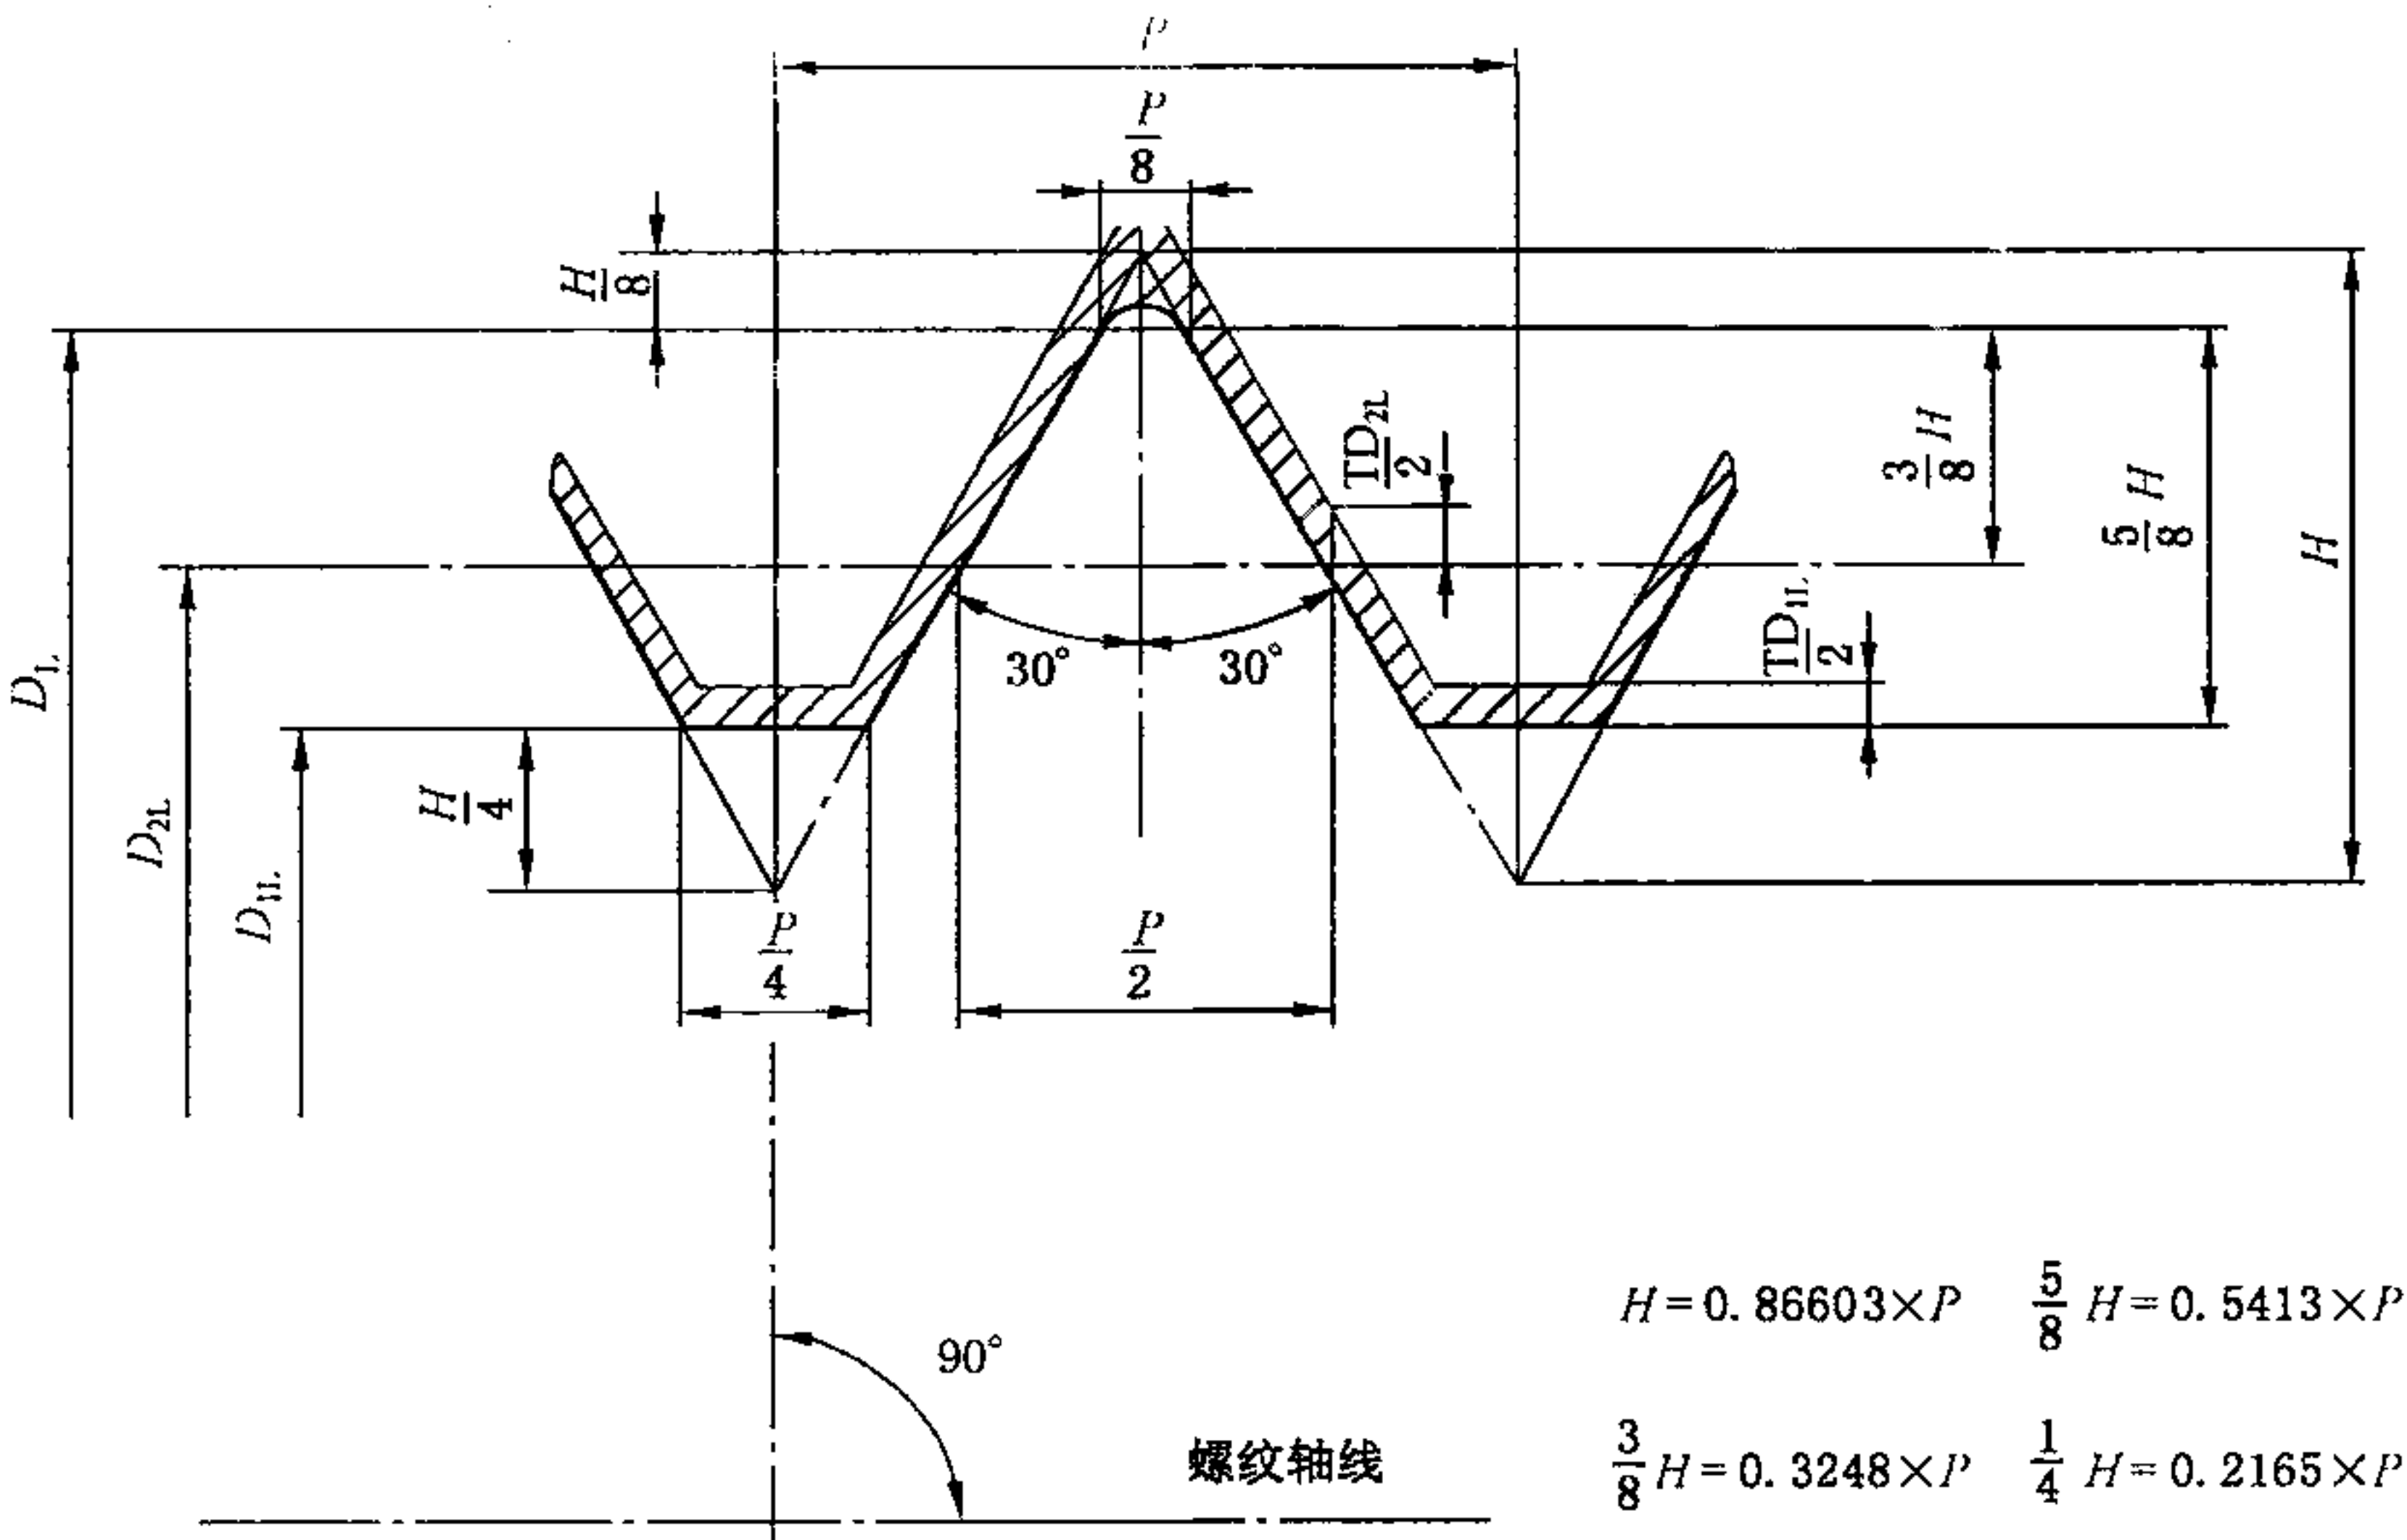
钢丝螺套用内螺纹基本牙型和公差带位置
